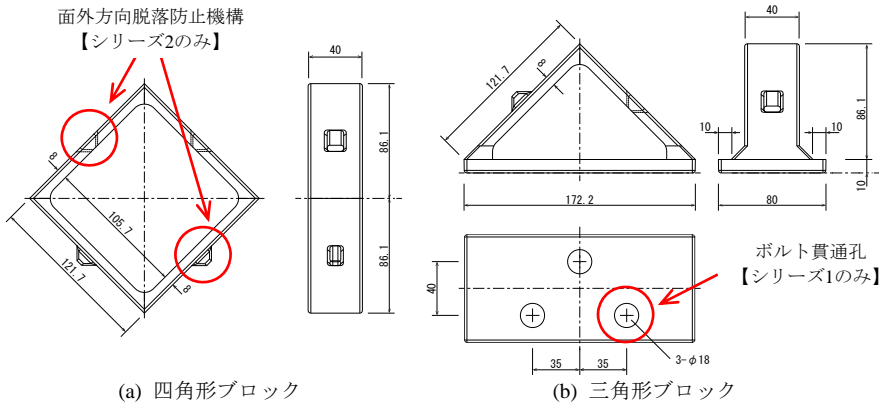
鋳鉄ブロック形状 Shapes of Casting Block
